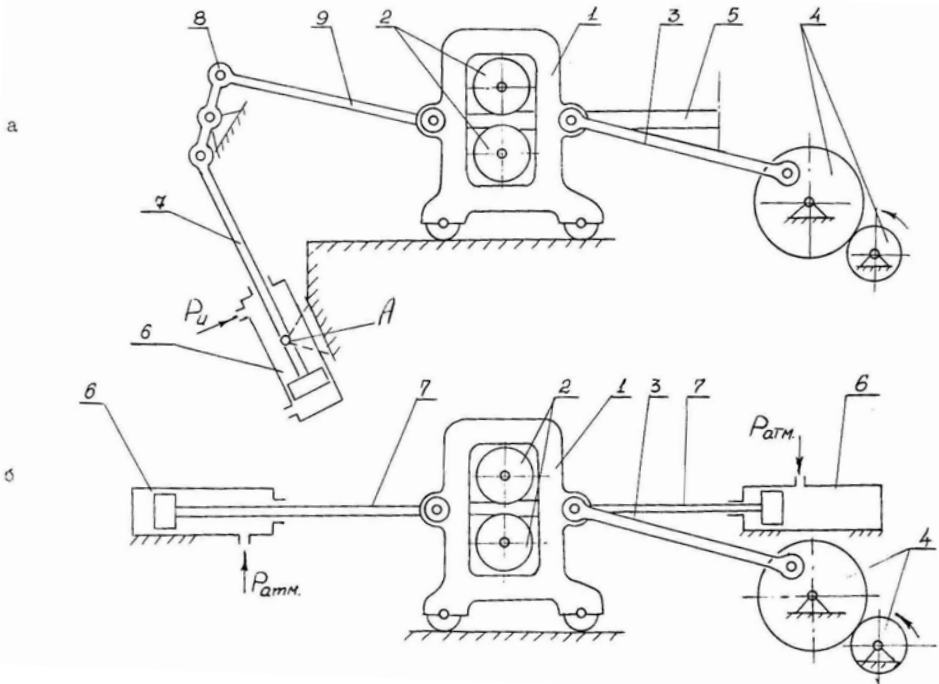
Схемы станов ХПТ с пневматическими уравнивающими механизмами
